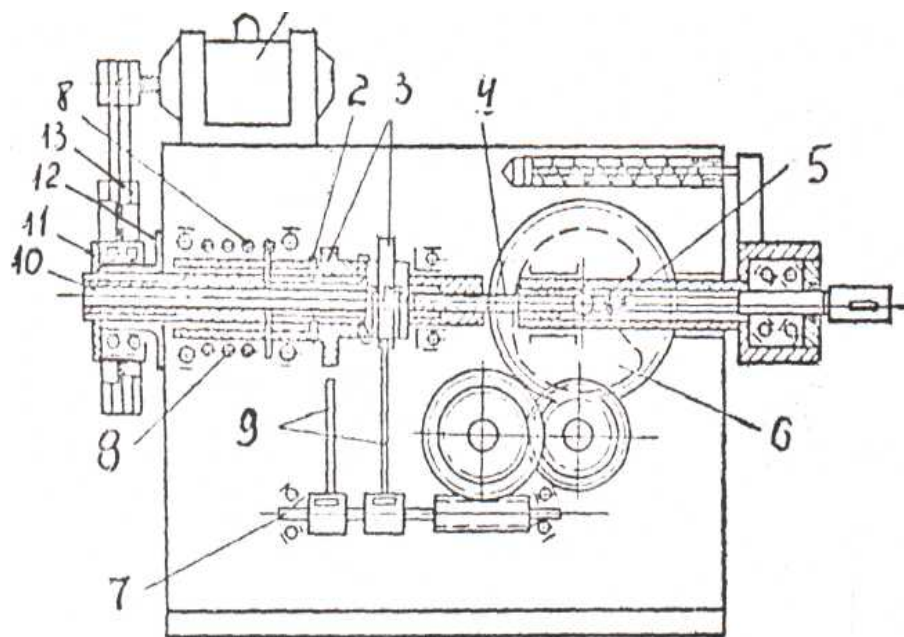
Схема кулачкового механізму для регулювання величини подачі
